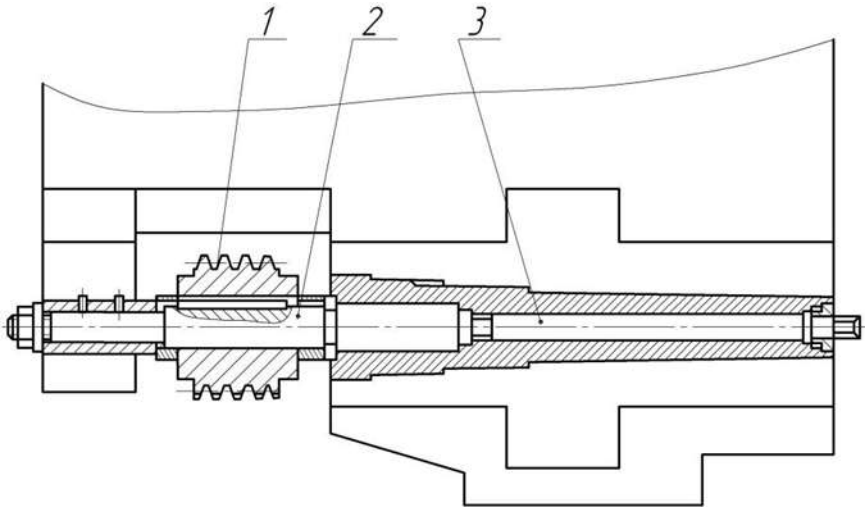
Схема розміщення черв'ячної фрези на оправці в супорті верстата:
